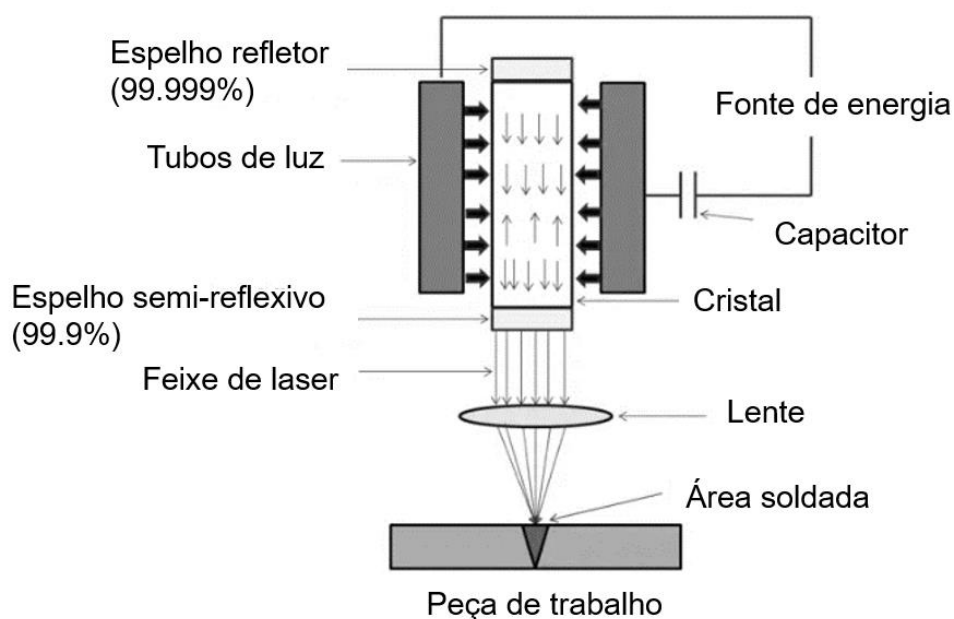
Esboço genérico de um equipamento de soldagem a laser. Fonte: adaptado de Chaturvedi (2021).
